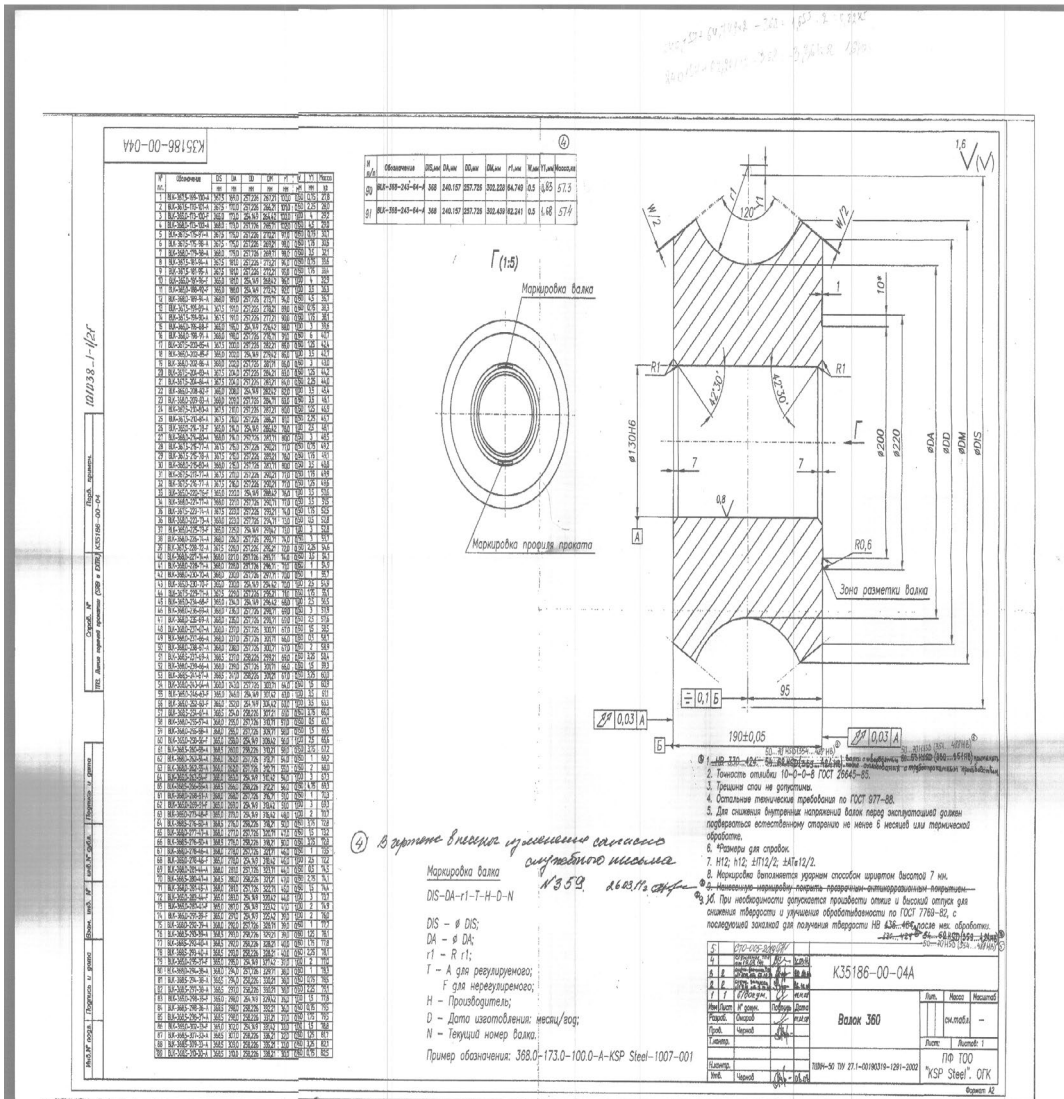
Общий вид отливки «Трубопрокатный валок» из чугуна ТШХН-50 [1]
